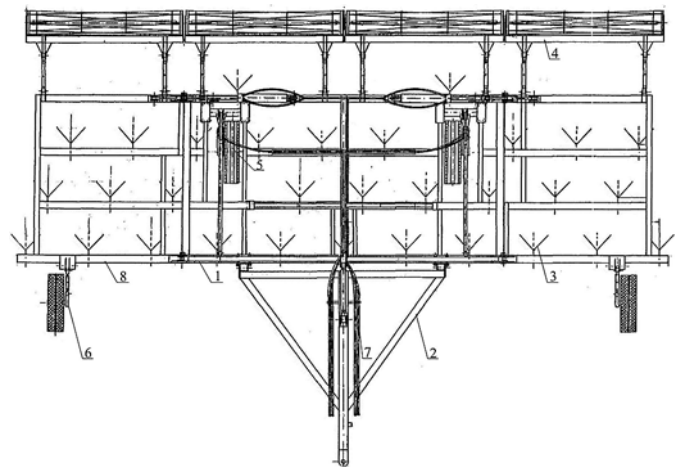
Конструкційна схема культиватора КСО-8: 1 – рама, 2 – причіпний пристрій, 3 – робочий орган, 4 – коток, 5 – опорно-транспортне колесо, 6 – опорне колесо, 7 – гідросистема, 8 – бокове крило
